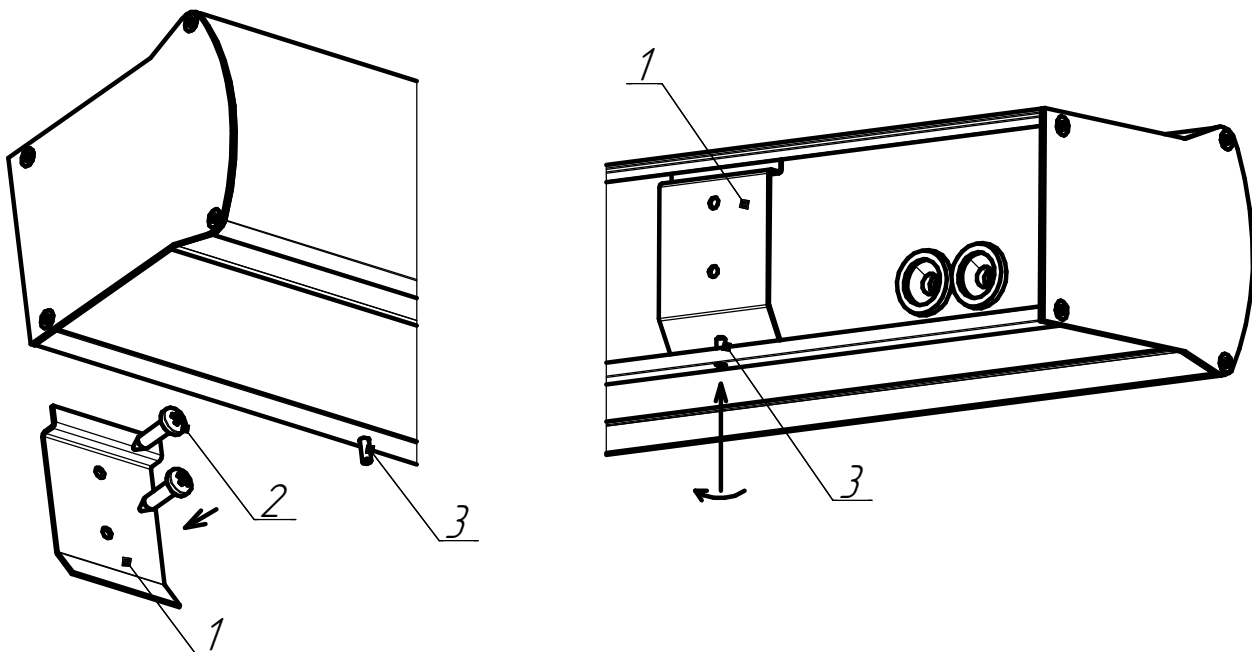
Крепление светильника ЛБО58 на стену.
